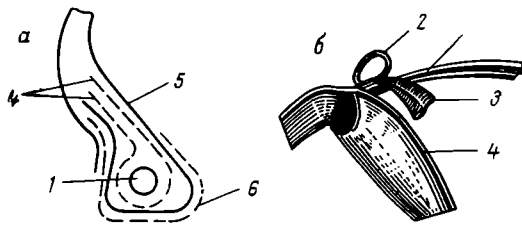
Борт малослойной легкой (а) и крыло многослойной грузовой (б) покрышек: 1 — бортовое кольцо; 2 — дополнительный шнур; 3 — лента для обертки; 4 — крыльевая лента; 5 — слой обрезиненного корда; 6 — бортовая лента.
